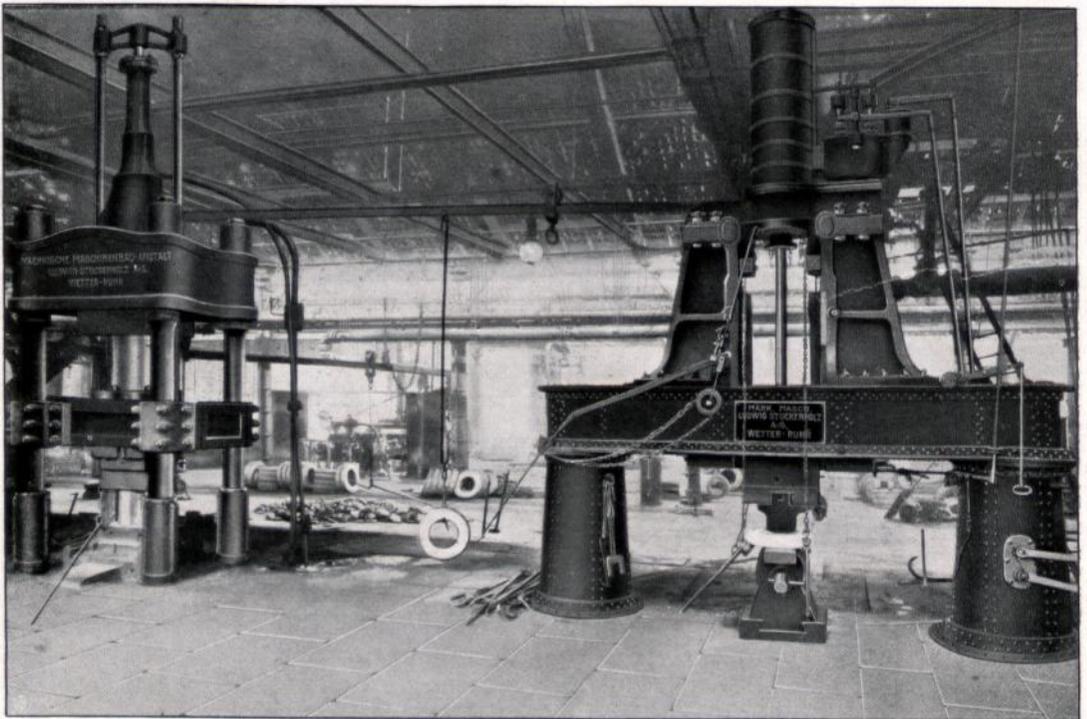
Druckwasser-Schmiedepresse (links) und Dampfhammer (rechts) zum Bearbeiten großer Schmiedestücke. Deutsche Maschinenfabrik, Duisburg.
